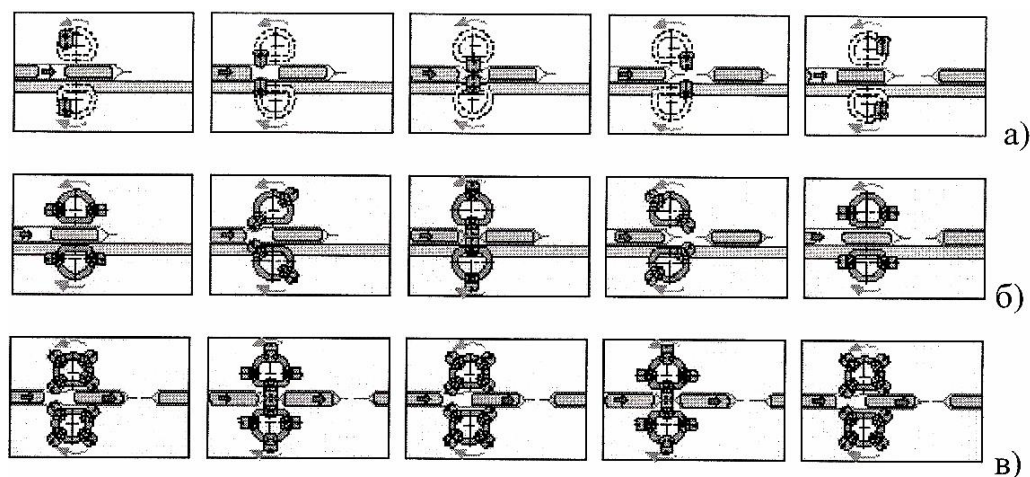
Схеми пристроїв зварювання – відрізування машин лінійного типу безперервної дії, що формують пакет типу «флоупак»: а – одна пара зварних елементів; б – дві пари; в – три пари.
